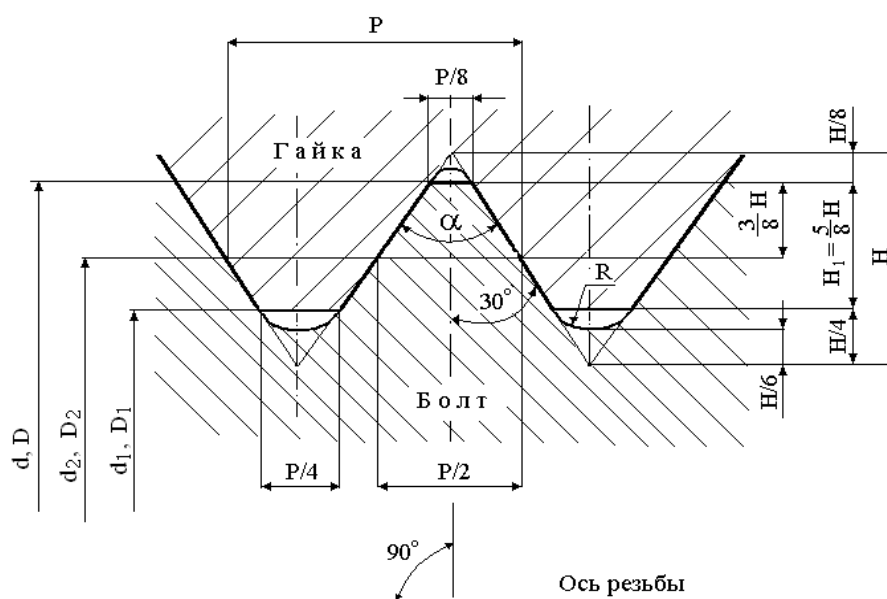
Профиль метрической резьбы и ее основные параметры
